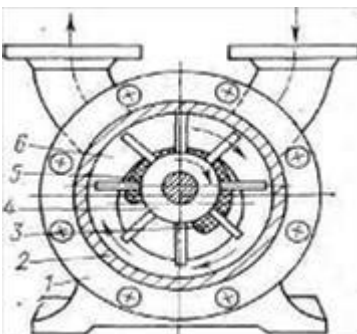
багатопластинчатой насоси: 1 - пластина; 2 - ротор.
